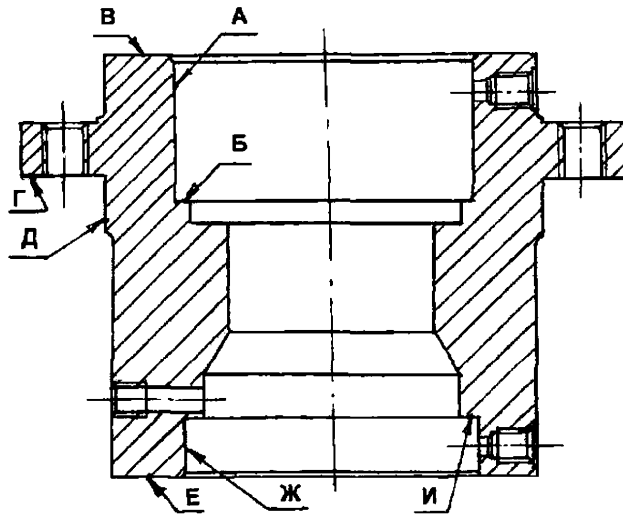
Корпус подшипника (поз. 7, рисунок 55)
